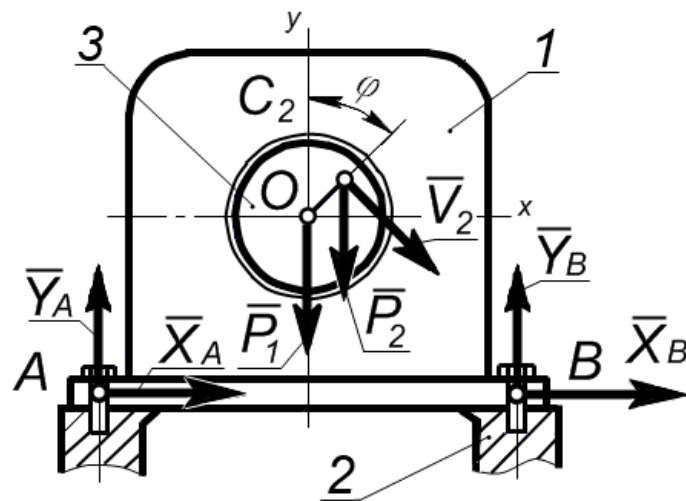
Розрахункова схема для визначення вертикального тиску та горизонтальних зусиль у болтових з'єднаннях коробки швидкостей з передньою тумбою
